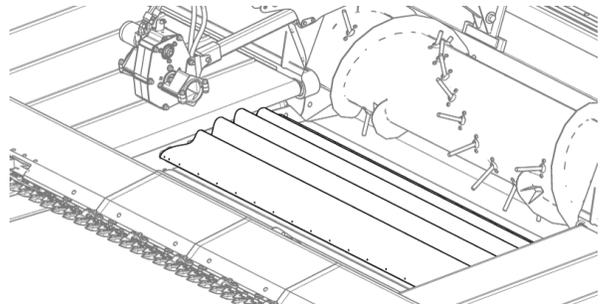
Neuen Draper auf dem Mitteldeck abrollen
